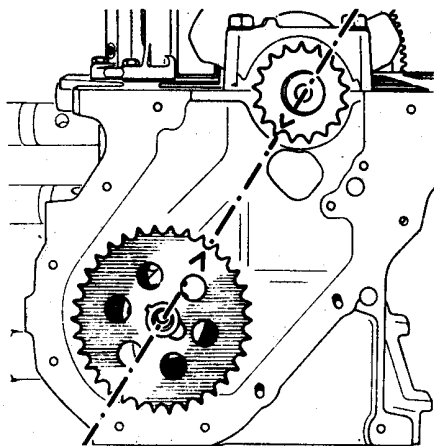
Las marcas de los engranajes, enfrentadas, coinciden con la línea de centro de los engranajes.
